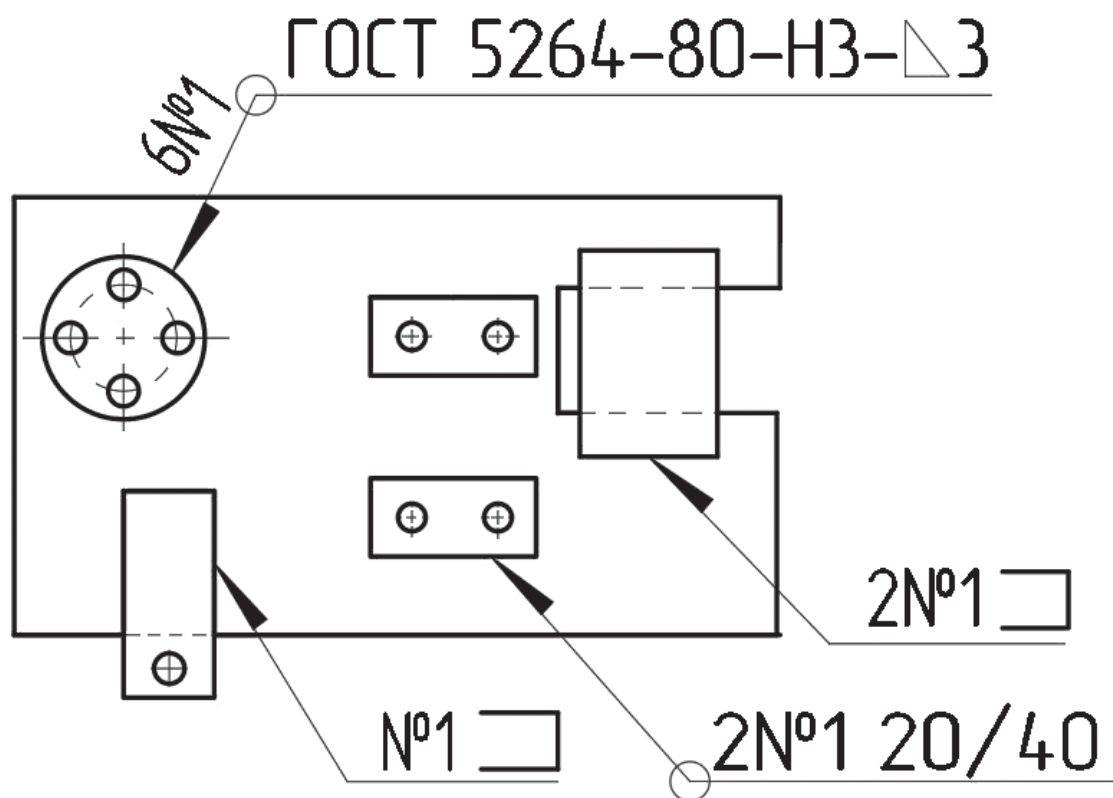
Упрощенное обозначение одинаковых сварных швов
